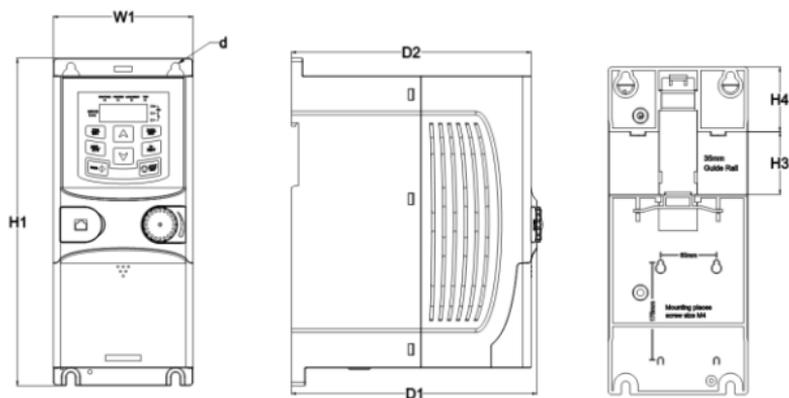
Montaje en carril DIN de los variadores de 0,4-2,2kW (dimensiones en mm)
